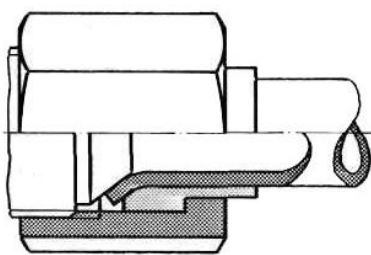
Різьбове з'єднання з ущільнювальною відбортовкою
